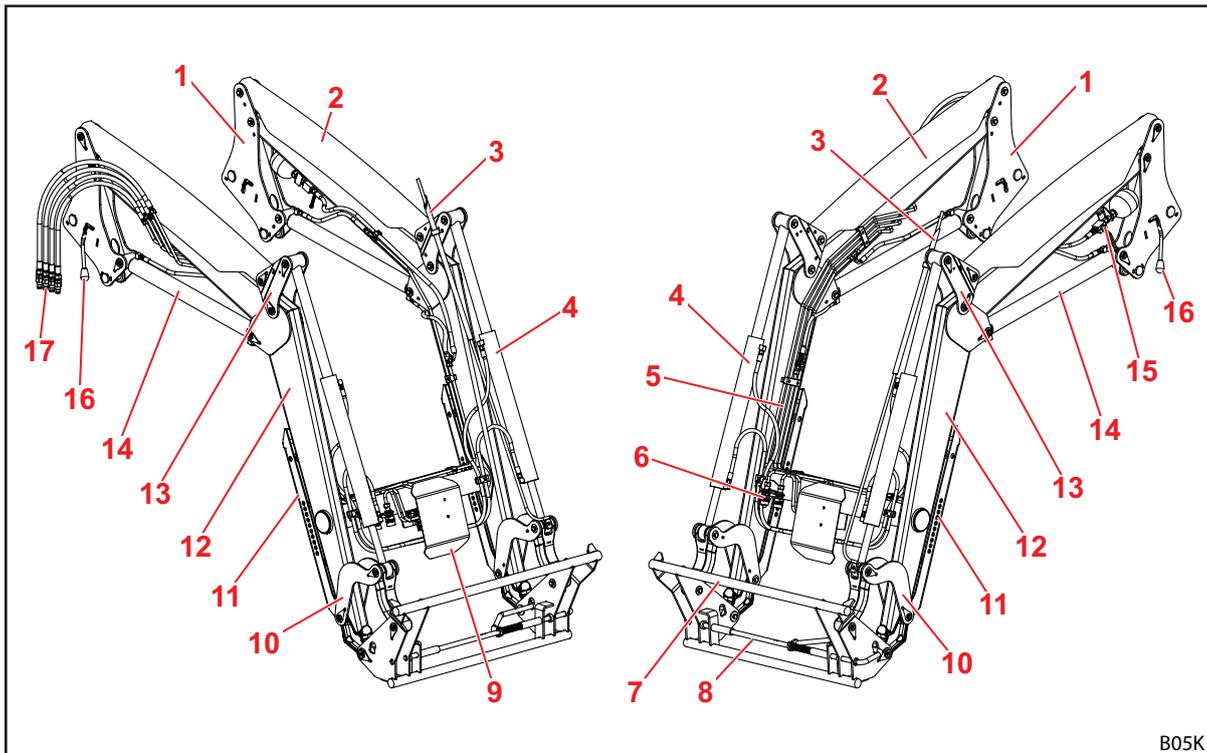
Caricatore frontale P (con guida parallela meccanica)
